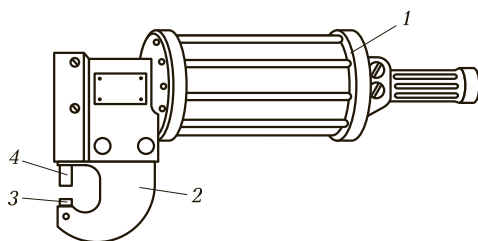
Ручной переносной пневматический пресс мод. ПРП5-2:
